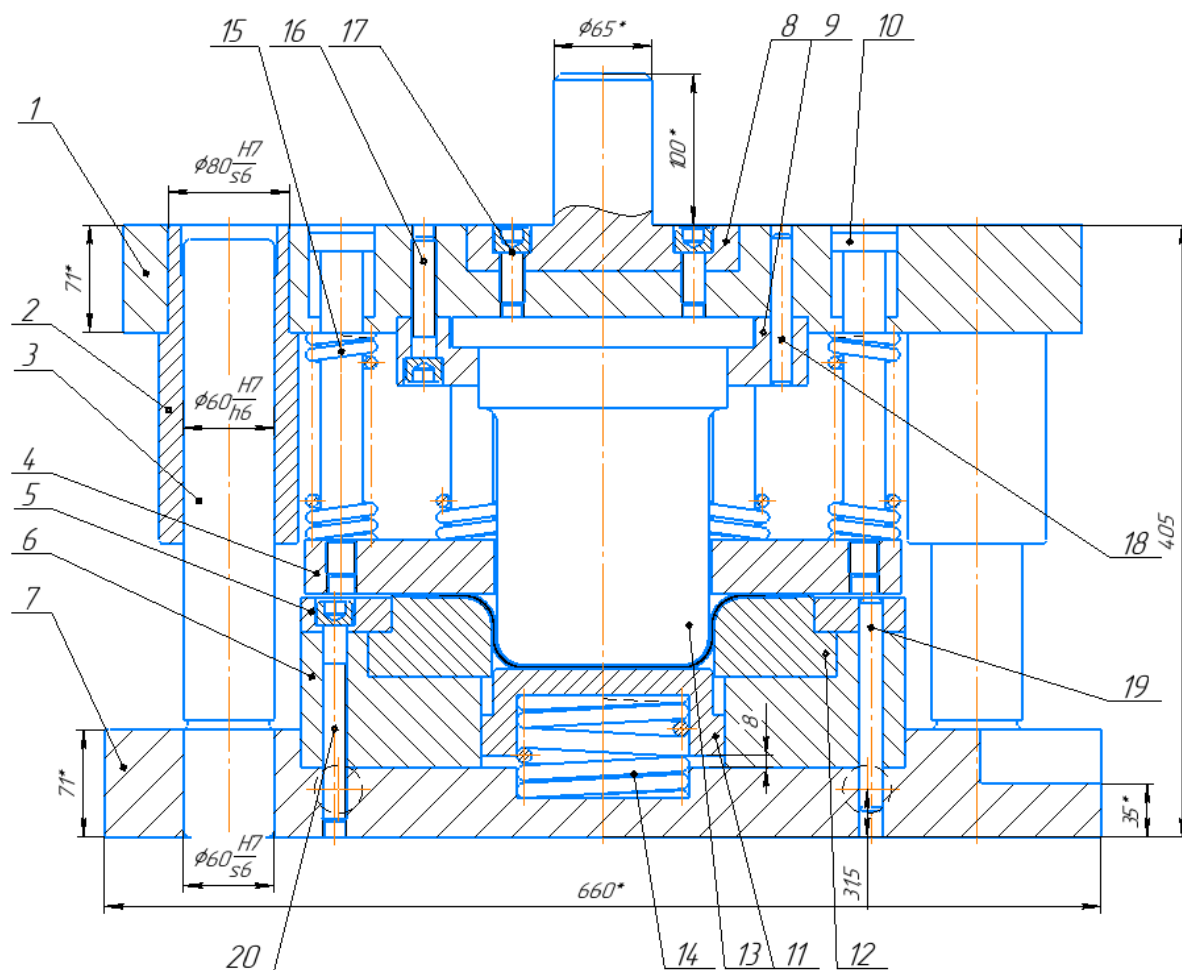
Общий вид штампа для первой вытяжки:
